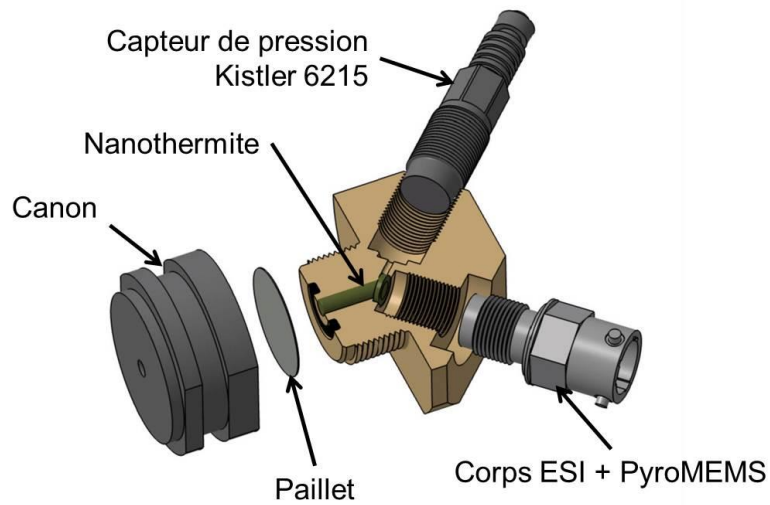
Vue éclatée en 3D du canon, du paillet et de la chambre de combustion (en coupe) intégrant de la nanothermite, un initiateur et un capteur de pression Kistler 6215.
